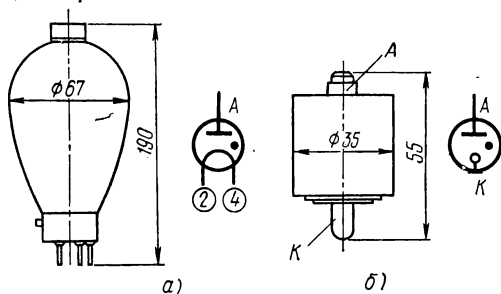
Габаритные чертежи и цоколевка газотронов:
